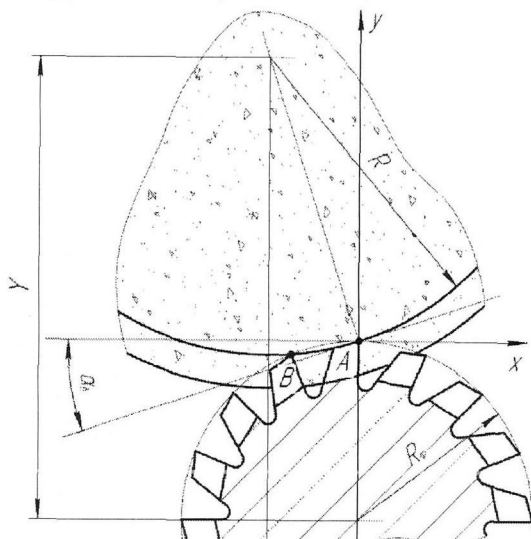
Схема к определению параметров установки шлифовального круга относительно заготовки червячной фрезы
